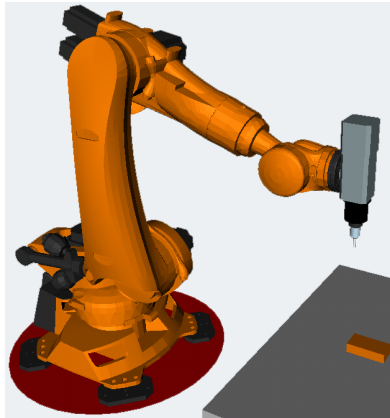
6-осевой робот со сгибающейся рукой и фрезерным шпинделем
